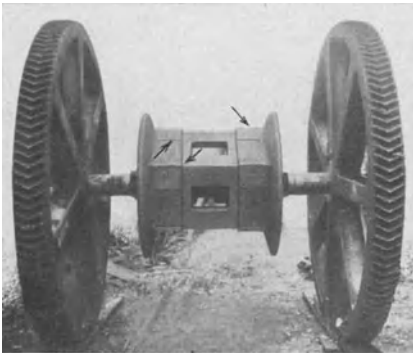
Auftragsschweißung an einer Kettentrommel.
